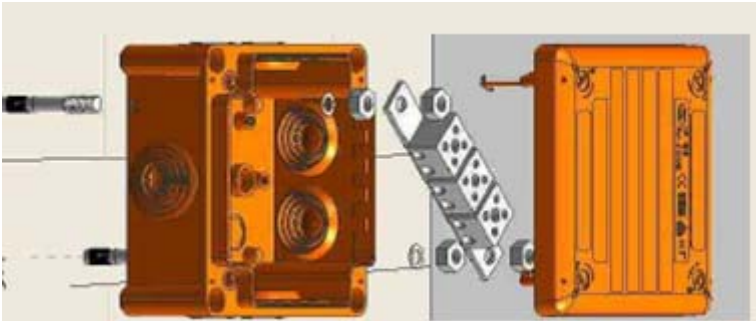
Схема монтажа коробки огнестойкой на бетонное основание
